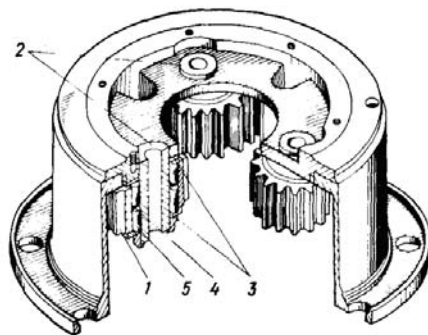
Разборка водила: 1 — сателлит; 2 — палец; 3, 4 — шайба; 5 — ролик
